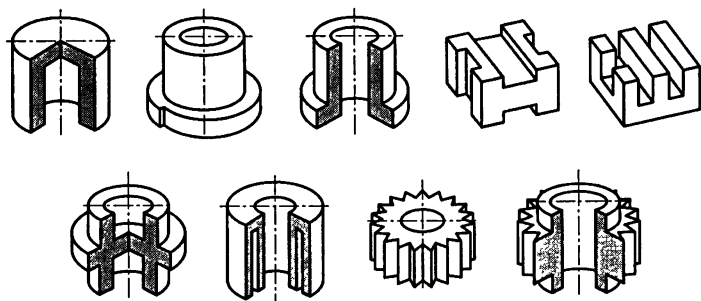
Типы заготовок, получаемых методом порошковой металлургии
